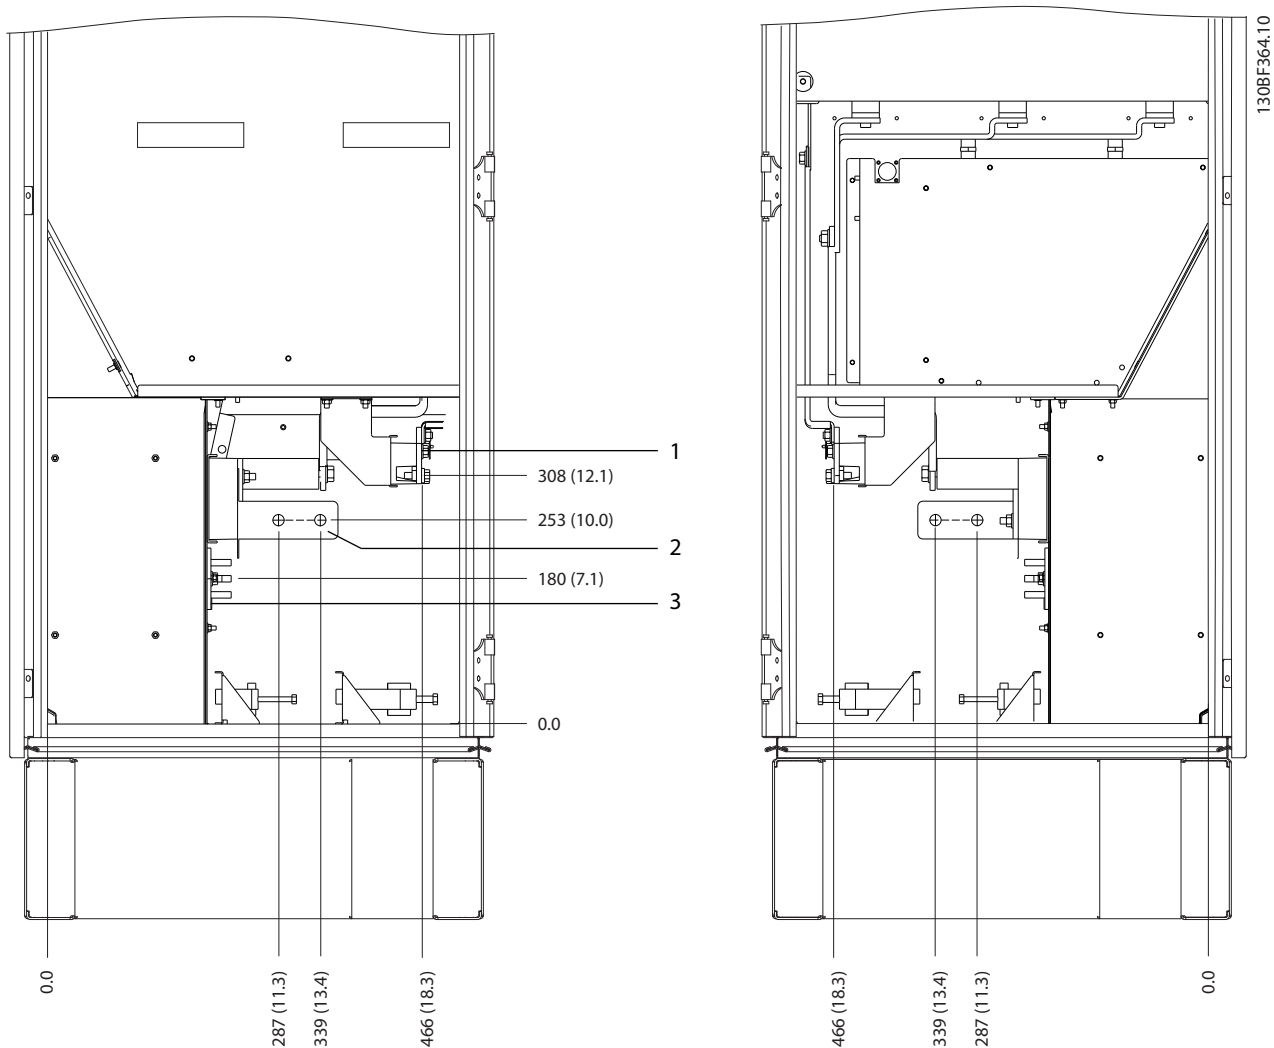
Размеры клемм для шкафа выпрямителя F1–F2, вид сбоку
